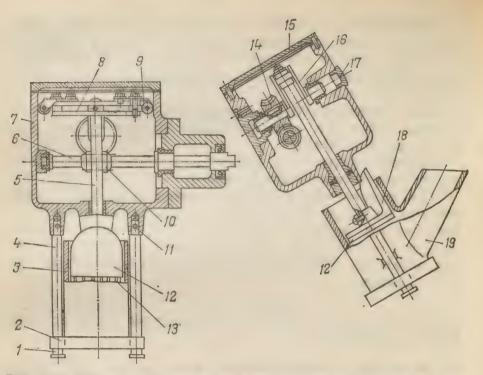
Пуансонный овощерезательный механизм МС 28-100 для нарезки сырого картофеля
